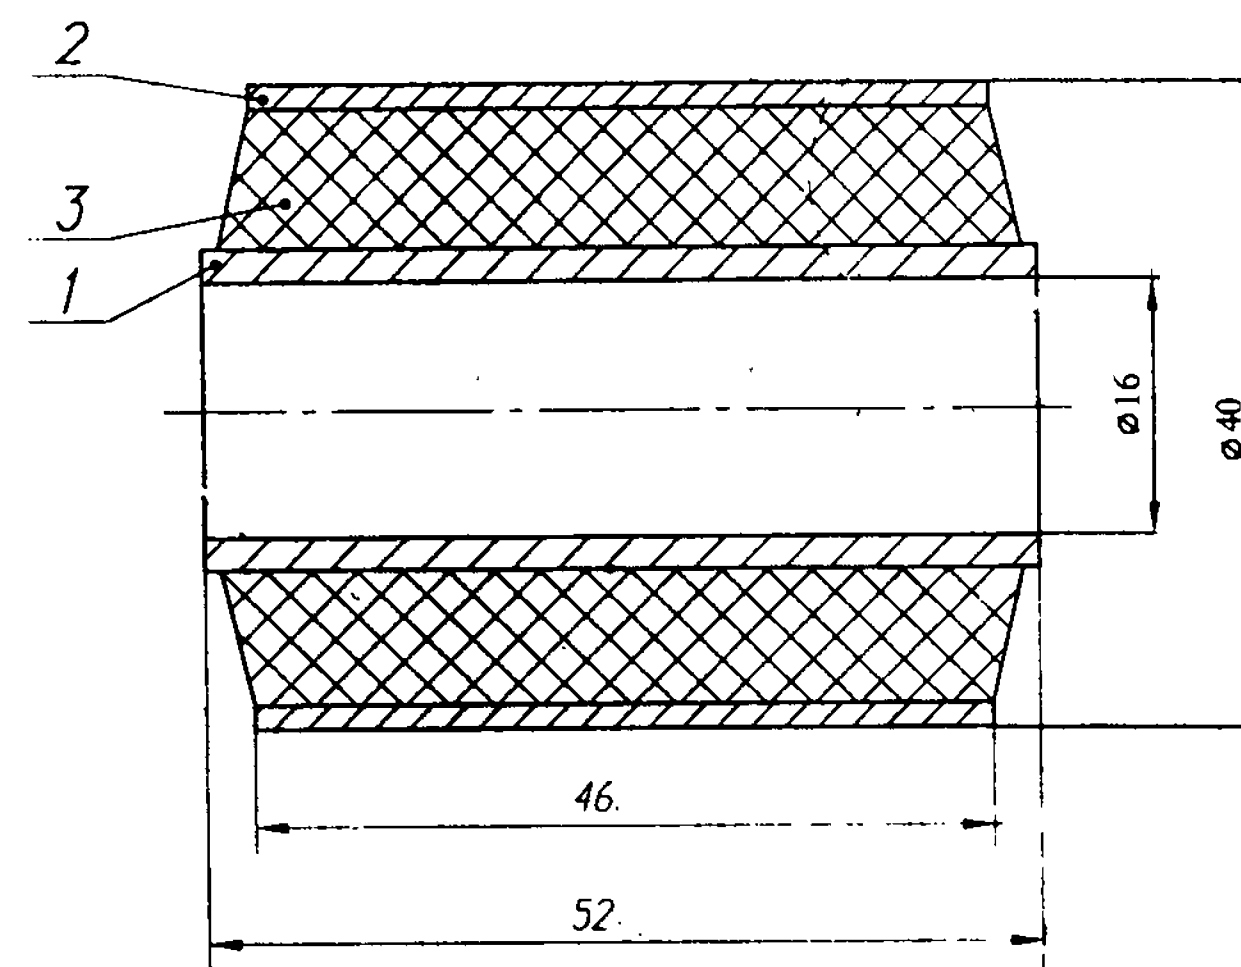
Сайлентблок верхнего рычага: 1 — обойма (втулка) внутренняя; 2 — обойма (втулка) наружная; 3 — резина
